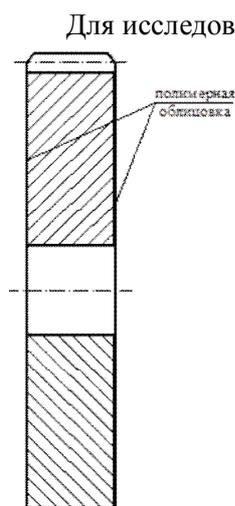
Металлополимерное зубчатое колесо: 1 – полимерная облицовка.
